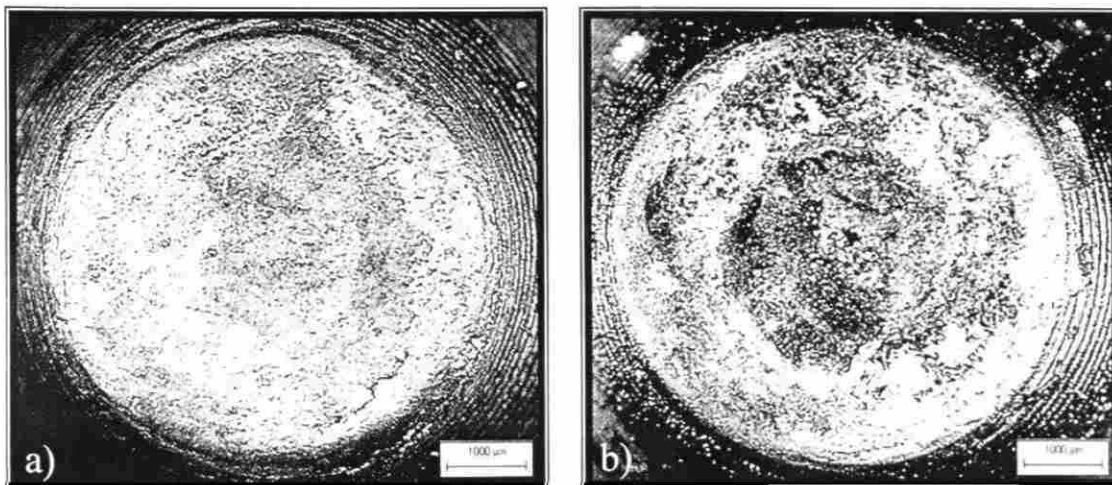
Cara de los electrodos al finalizar la prueba de calidad de soldadura.
